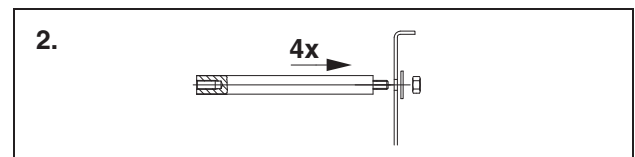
Distanzbolzen durch die Bohrungen stecken und befestigen
